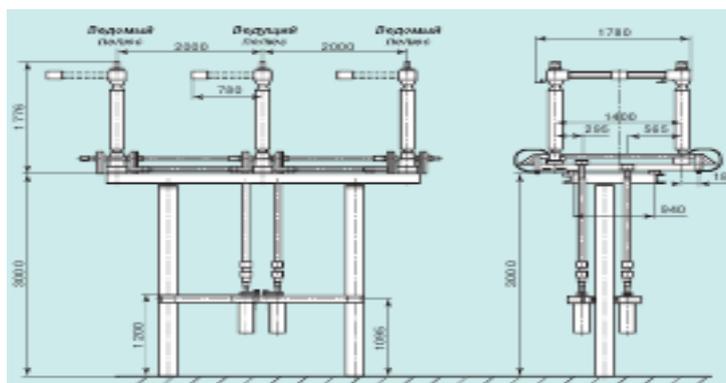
Общий вид, габаритные установочные размеры разъединителя РГД-110
